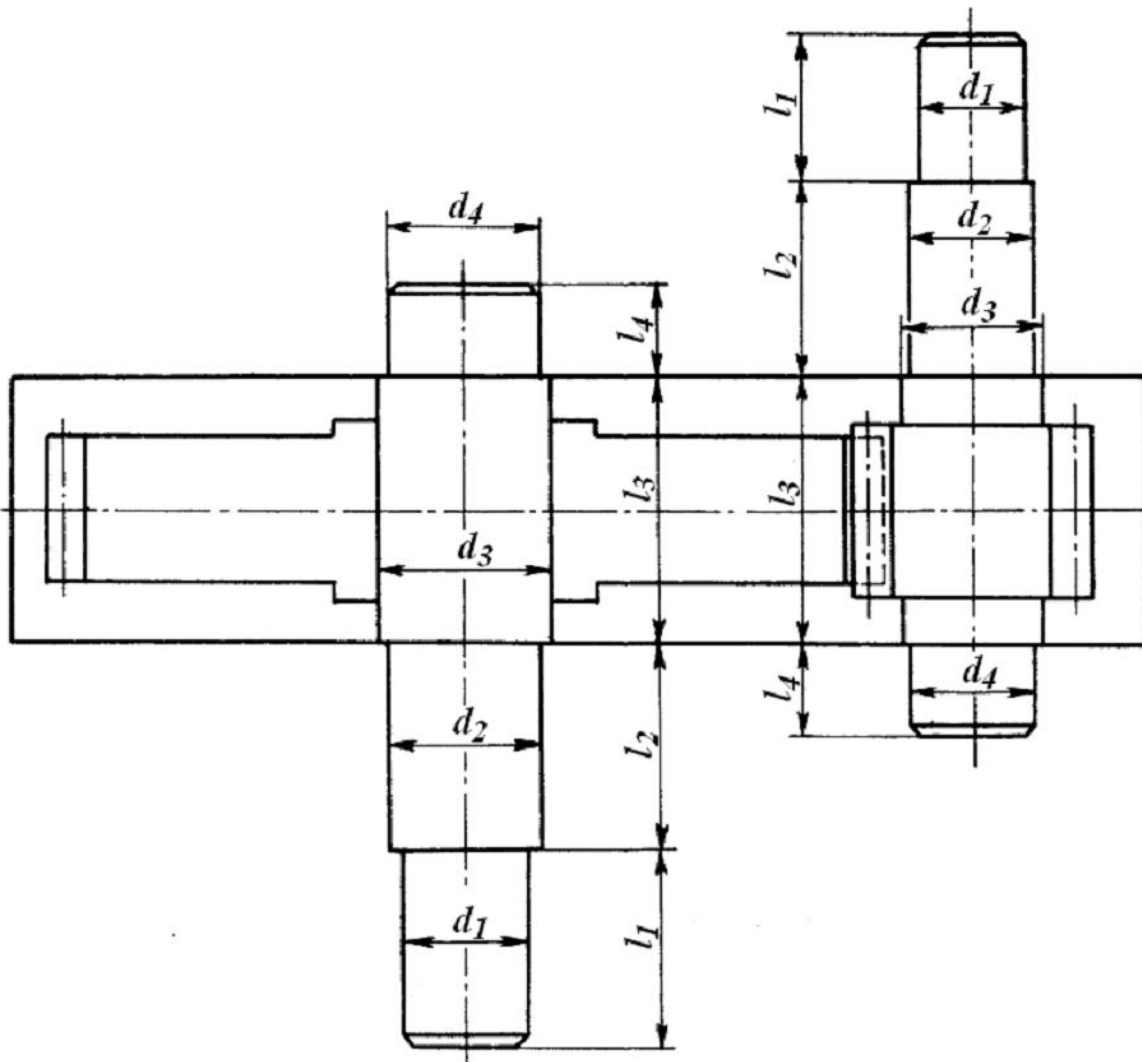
Последовательность разработки чертежа общего вида редуктора
